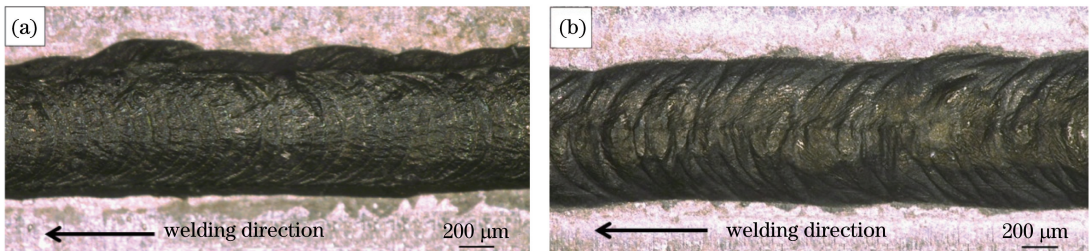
焊缝表面形貌。(a)上表面;(b)下表面
